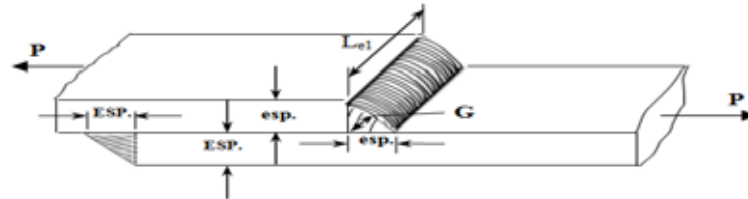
Soldaduras de ángulo, sometida a tracción, entre dos láminas de distinto espesor ($ESP. > esp.$); G es el área de garganta de cada cordón de soldadura, tomado en cada caso particular.
